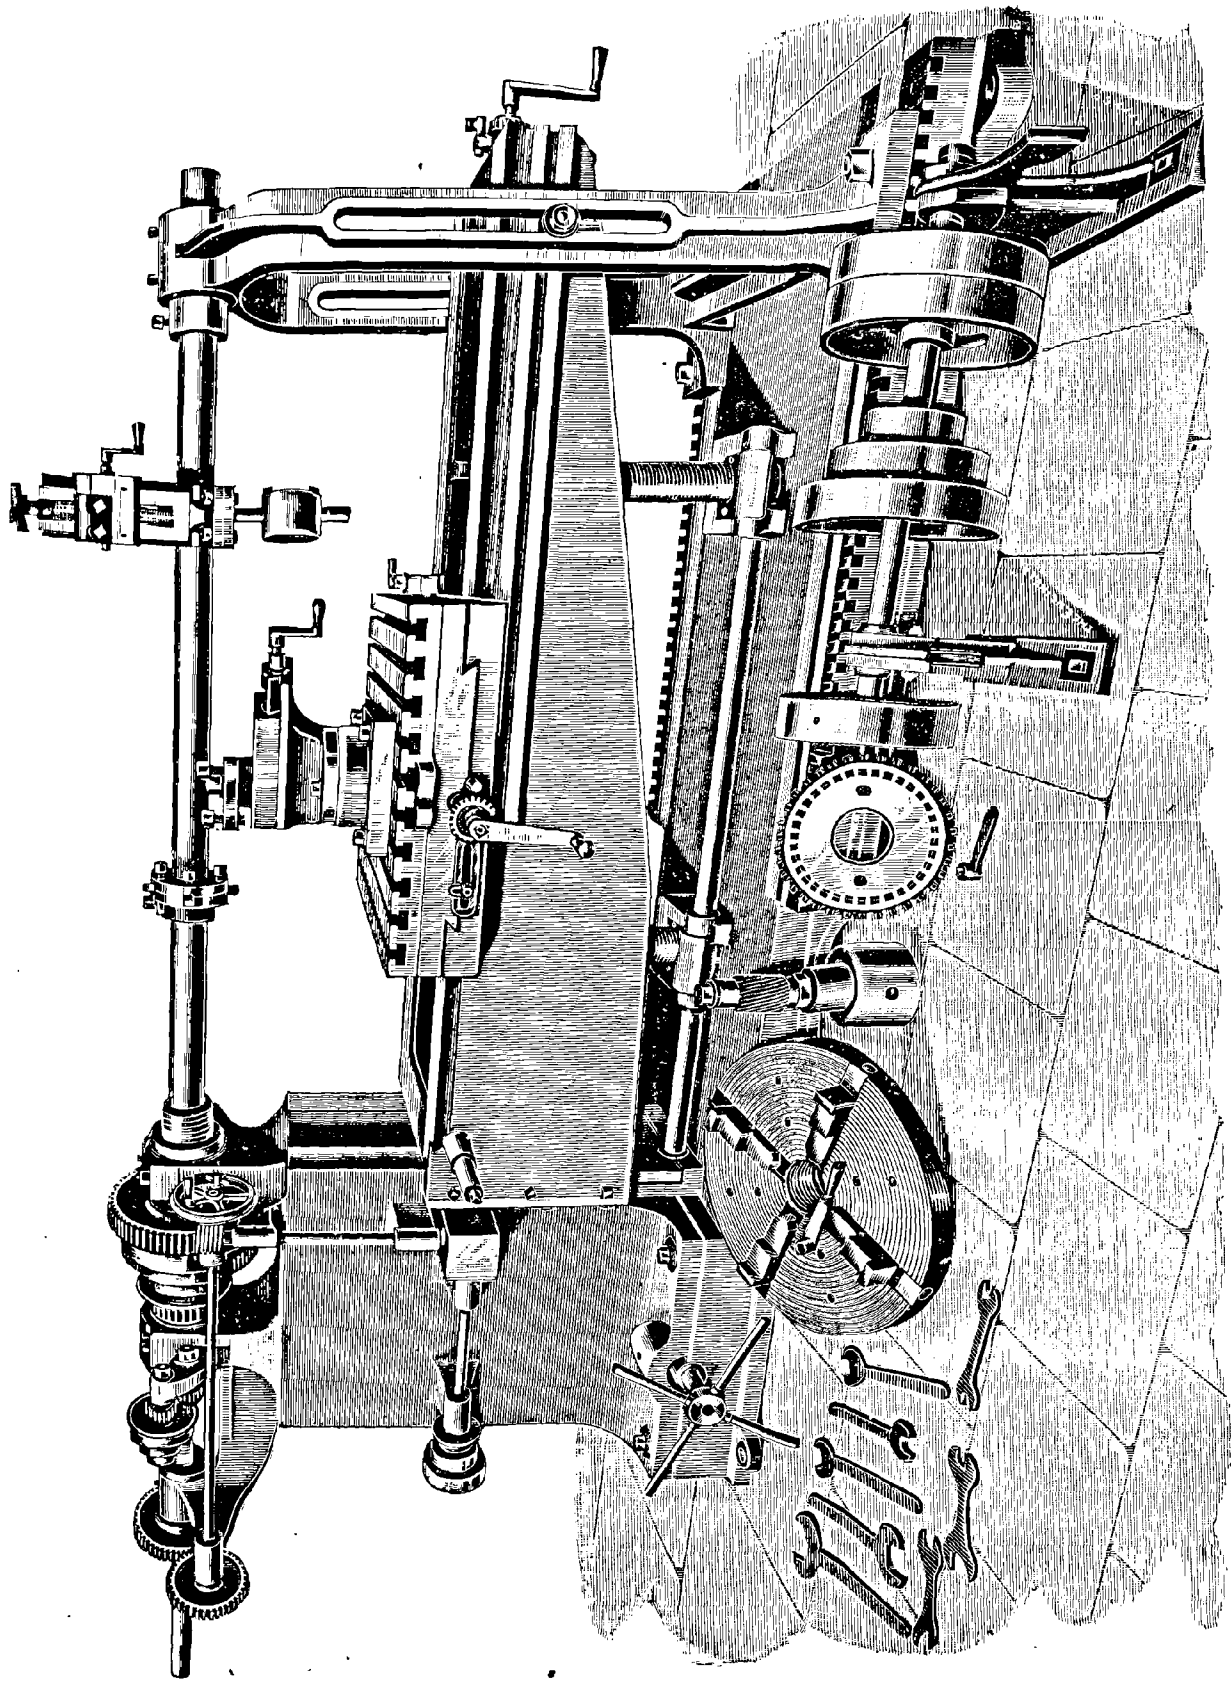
Machine à aléser, surfacer et fraiser horizontale de M. Lucas.
